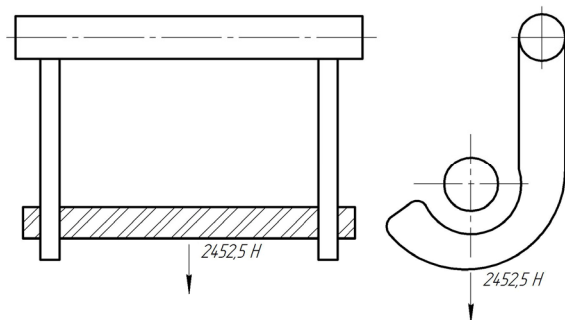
Схема проверки прочности механизма останова при воздействии статической нагрузки
